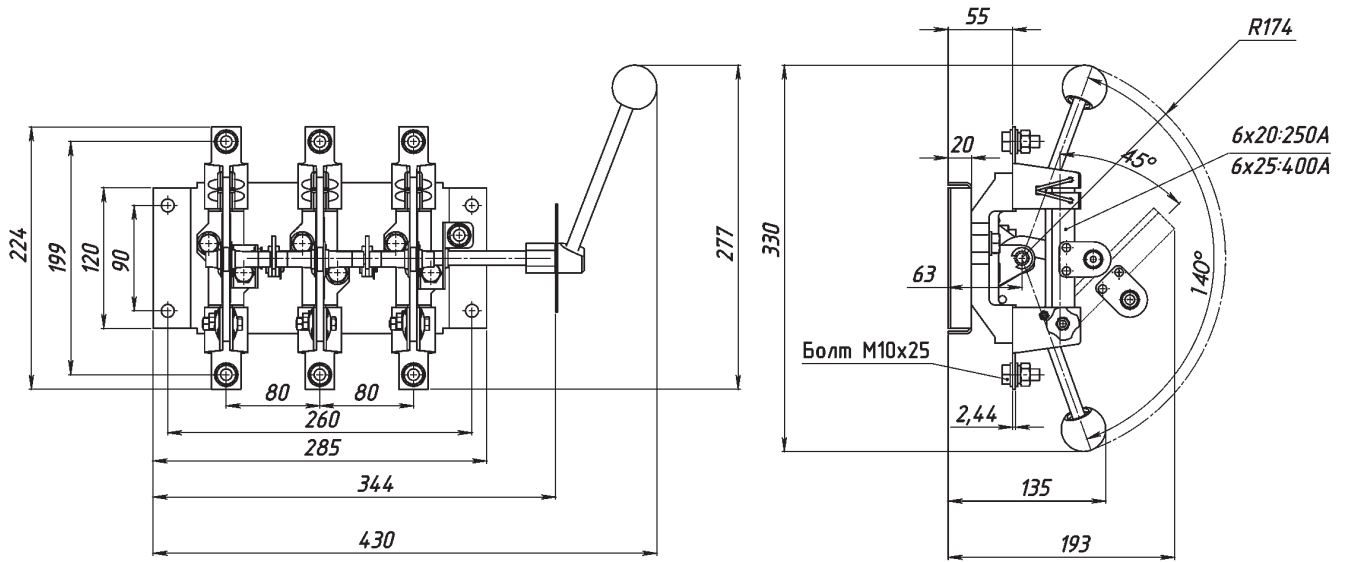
Разъединитель серии Р с боковой ручкой РБ-2, РБ-4, на номинальный ток 250 А и 400 А
